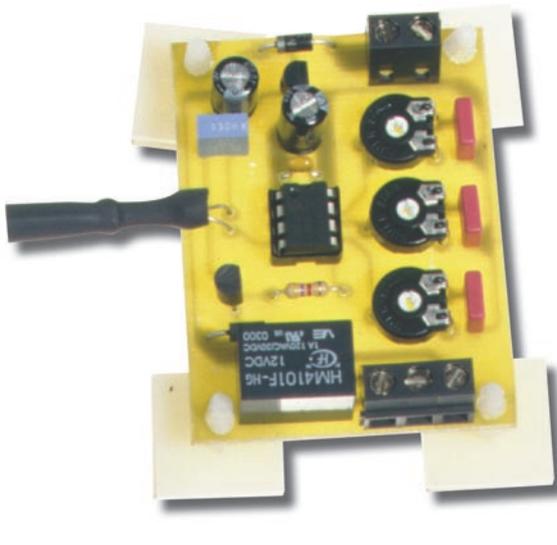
Photo d'un des prototypes du capteur optique de mouvement.
